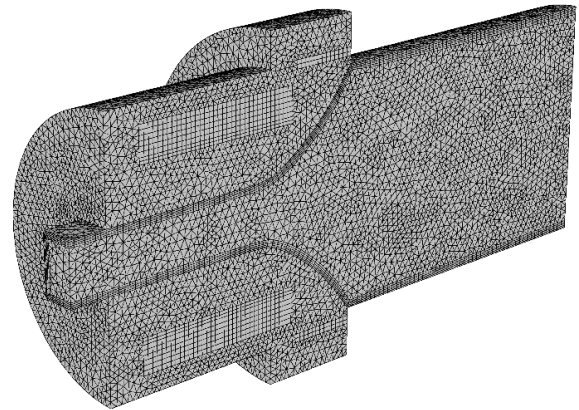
Дискредитована модель пресового інструменту для формування великогабаритних вуглецевих заготовок
